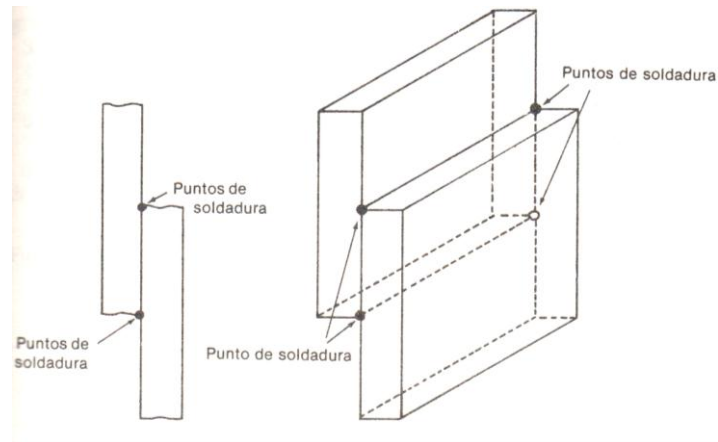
Traslape de la placa de $\frac{1}{4}$ de espesor y unión por puntos de soldadura.
